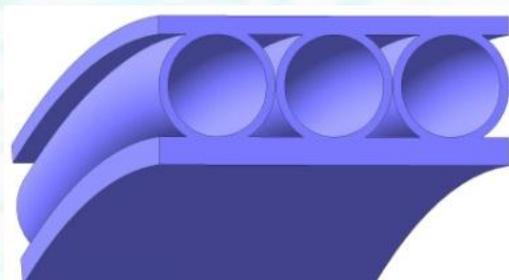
Изготовление трёхслойных труб для ёмкостей круглого и квадратного сечения
